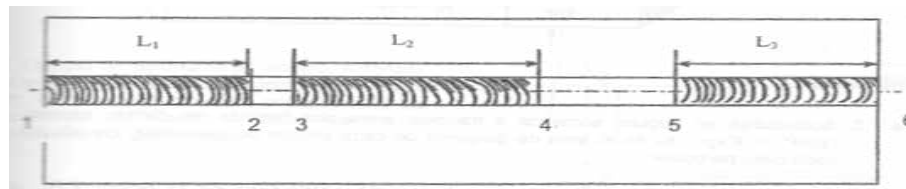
Soldadura a tope con bisel, con seis extremos en el cordón.
